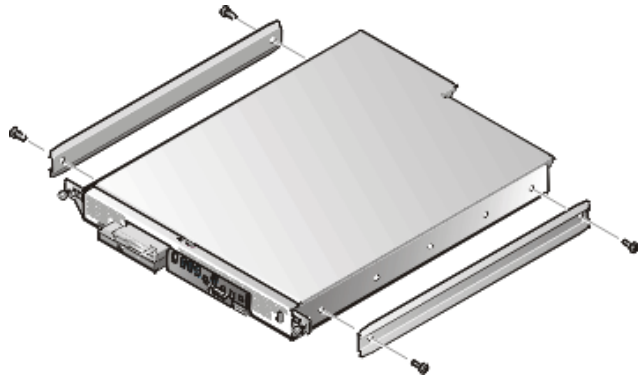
Befestigung der Innen-Schienen am System-Chassis
